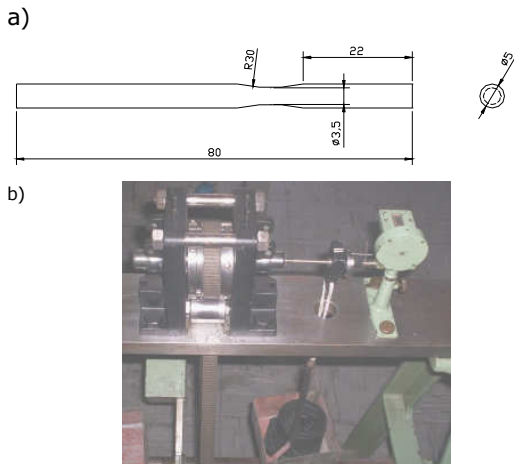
a) Geometría y dimensiones de la probeta de fatiga empleada, b) máquina de fatiga por flexión rotativa.
